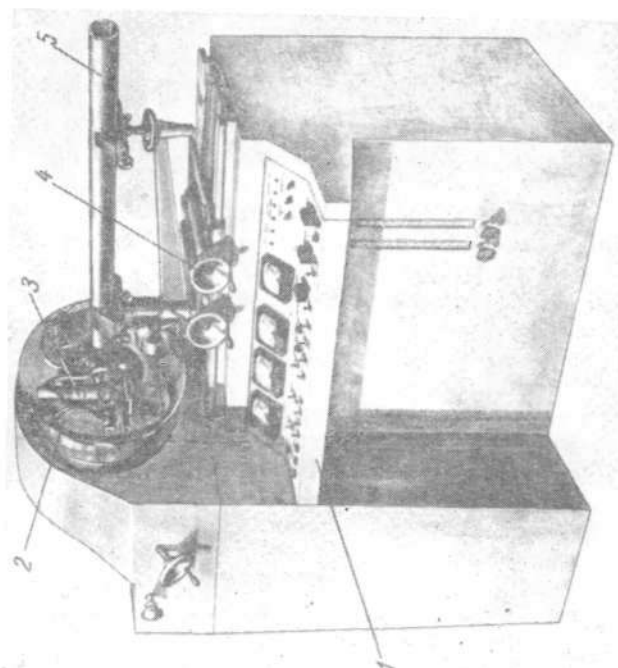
Автомат АСТА для сварки стыков труб и арматуры с трубами.
